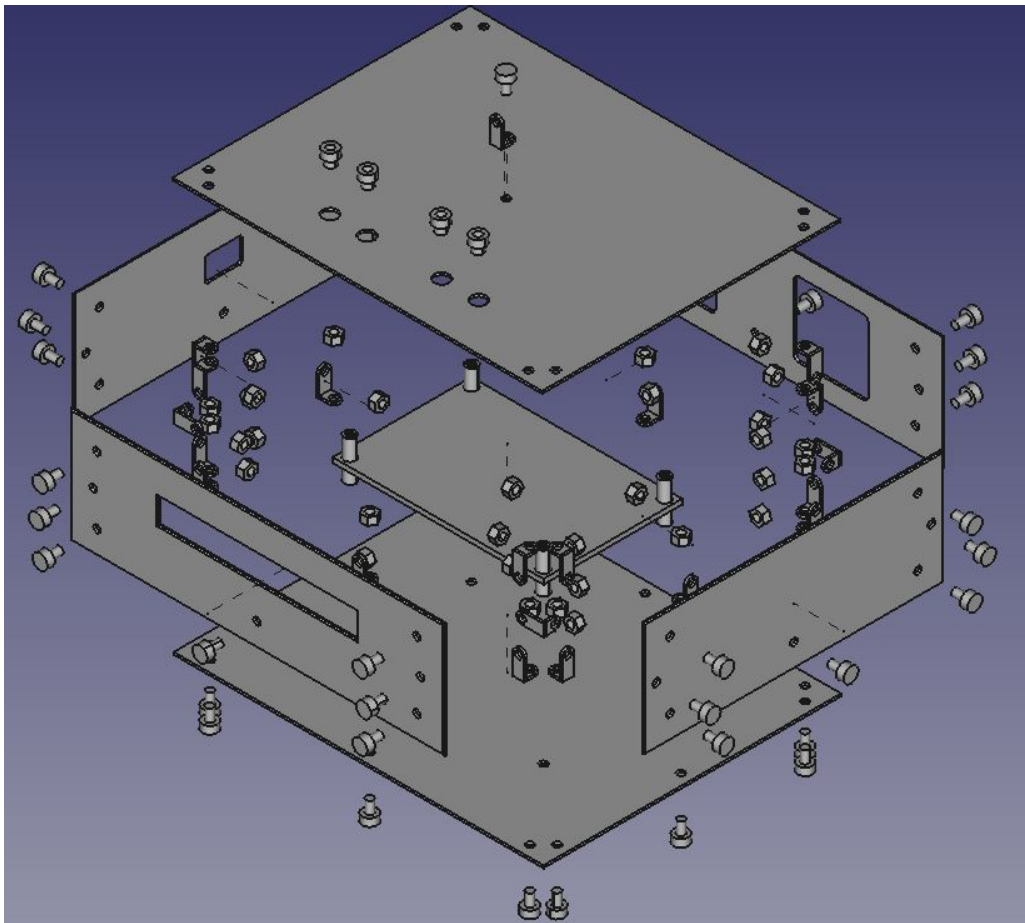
Vista explosionada de la Carcasa, creado con FreeCAD.
